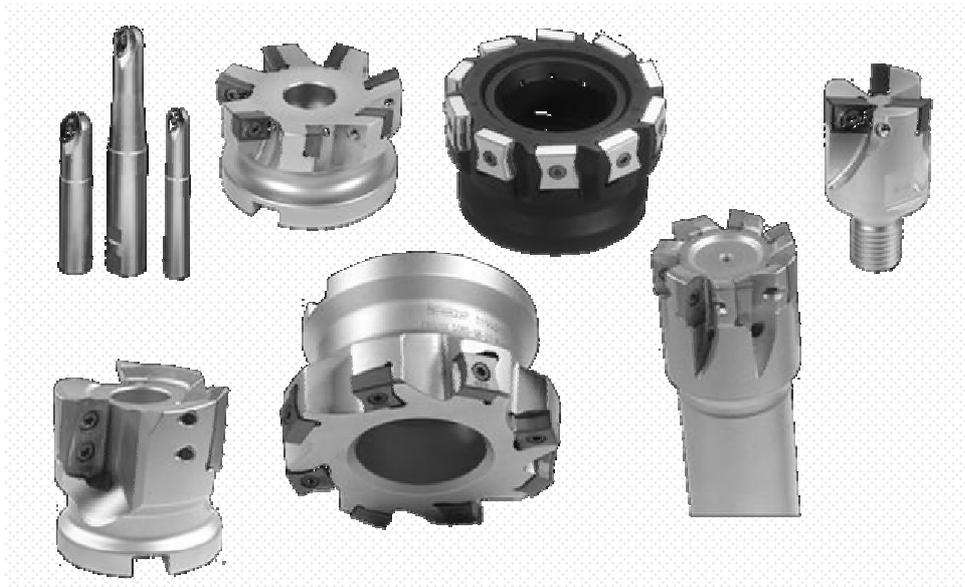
Фрезы концевые и торцовые с механическим креплением твердосплавных пластин
